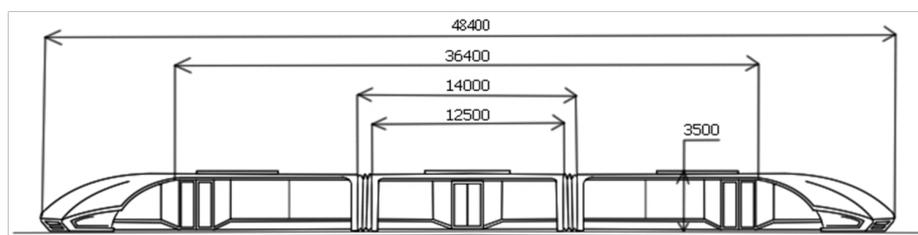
Габаритные размеры разрабатываемого рельсового транспорта
